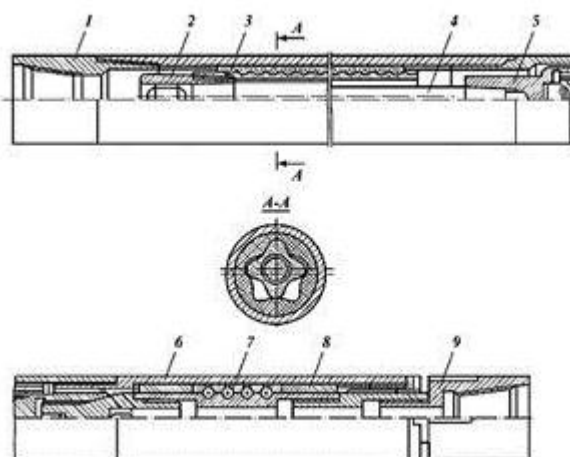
Винтовой забойный двигатель типа ДГ-108
